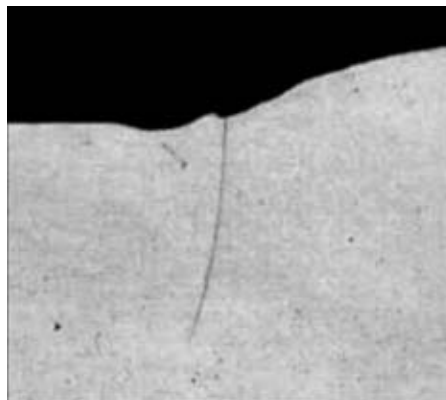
Вид сбоку образца с трещиной усталости, образовавшейся в зоне напыла металла в результате отступления от технологии проковки сварного шва
